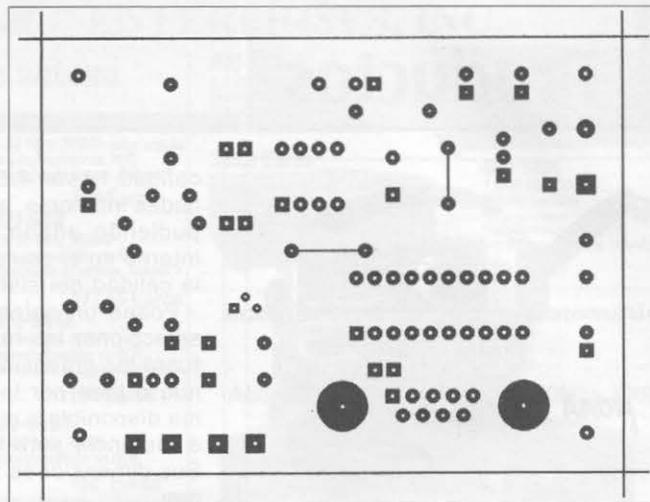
Plantilla de serigrafía. Lado de soldaduras.
